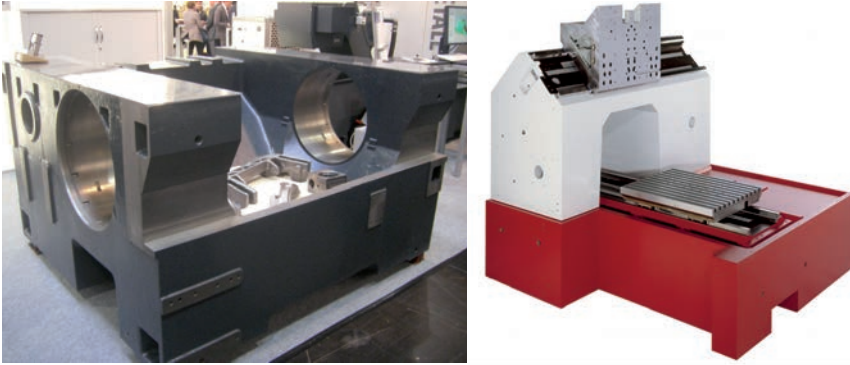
Estructuras de máquinas monobloque. Izda. Bancada fundida por Alzmetall®.
